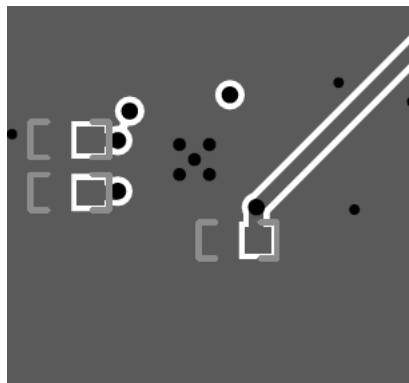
LMK3H0102 の PCB レイアウト例、最下層
